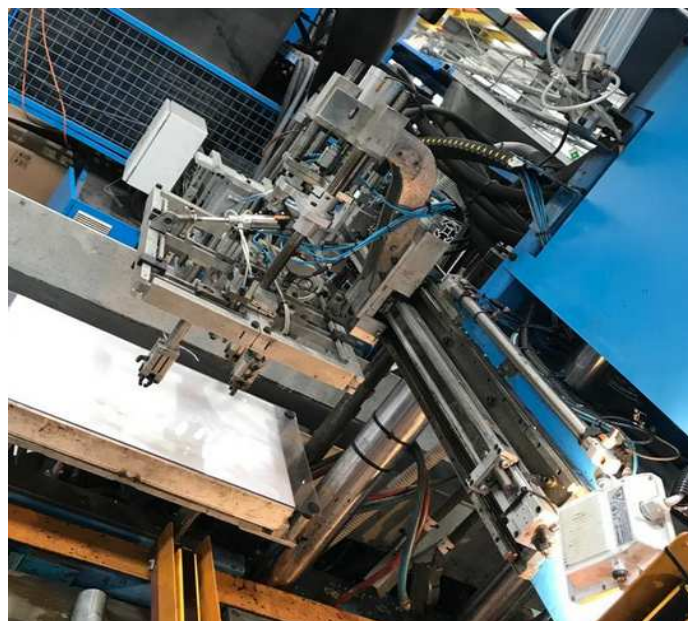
Robô manipulador das máquinas de injeção de plástico.
